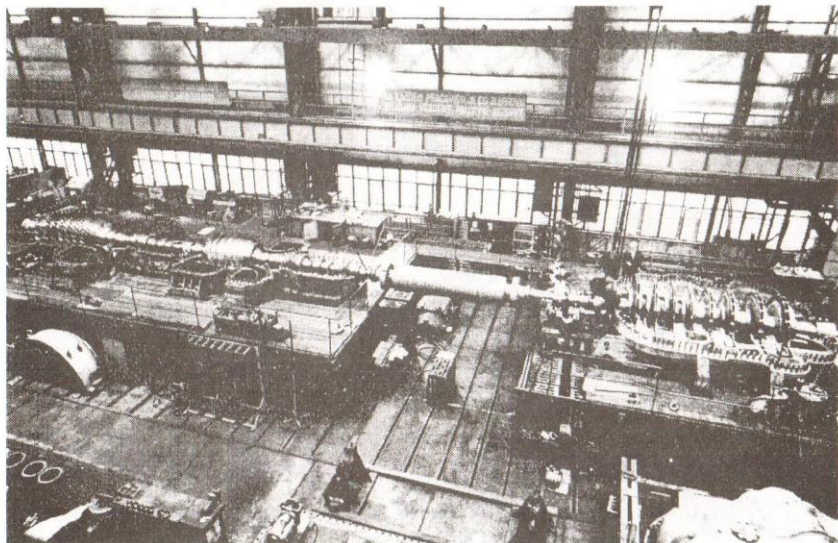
Radiální turbokompresor ze soustrojí Bajkal se stlačněním 12
